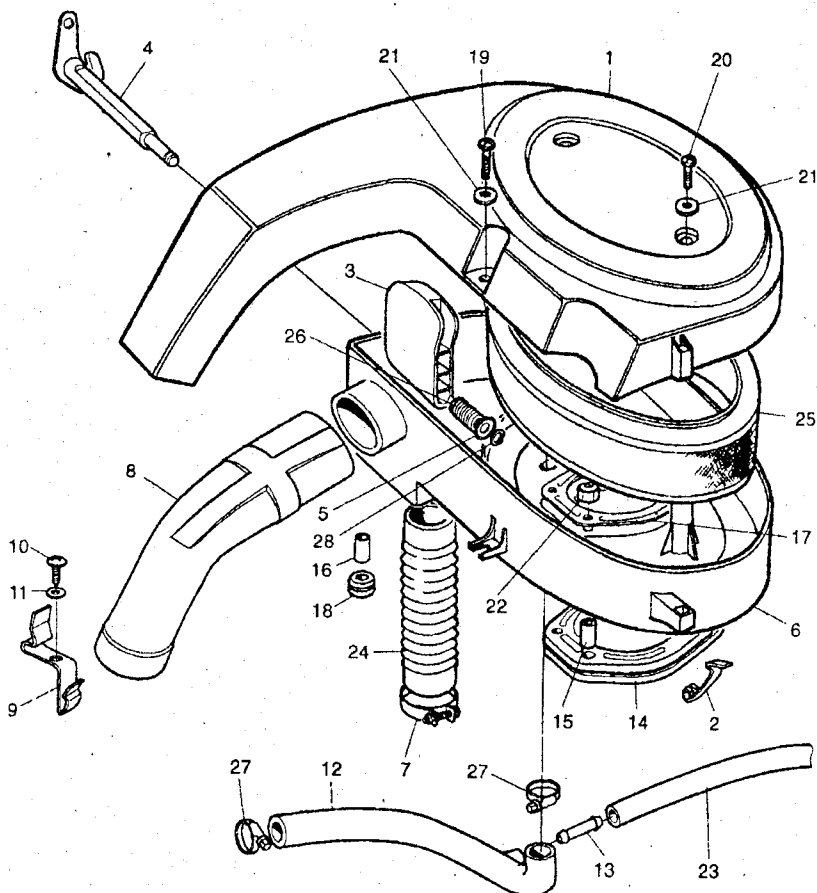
Воздушный фильтр и заборник теплого воздуха двигателей MeMZ-2457 (1.2 L) и MeMZ-3011 (1.3 L): 1 – крышка; 2 – защёлка крышки; 3 – заслонка в сборе; 4 – рычаг в сборе; 5 – шайба специальная; 6 – корпус в сборе; 7 – зажим; 8 – заборник холодного воздуха; 9 – фиксатор; 10 – винт; 11 – шайба; 12 – шланг отсоса картерных газов; 13 – трубка соединительная; 14 – прокладка; 15, 16 – втулка; 17 – накладка; 18 – подушка; 19, 20 – винт; 21 – шайба; 22 – гайка; 23 – шланг вентиляции картера; 24 – шланг гофрированный; 25 – фильтрующий элемент; 26 – пружина; 27 – хомут; 28 – шайба стопорная
